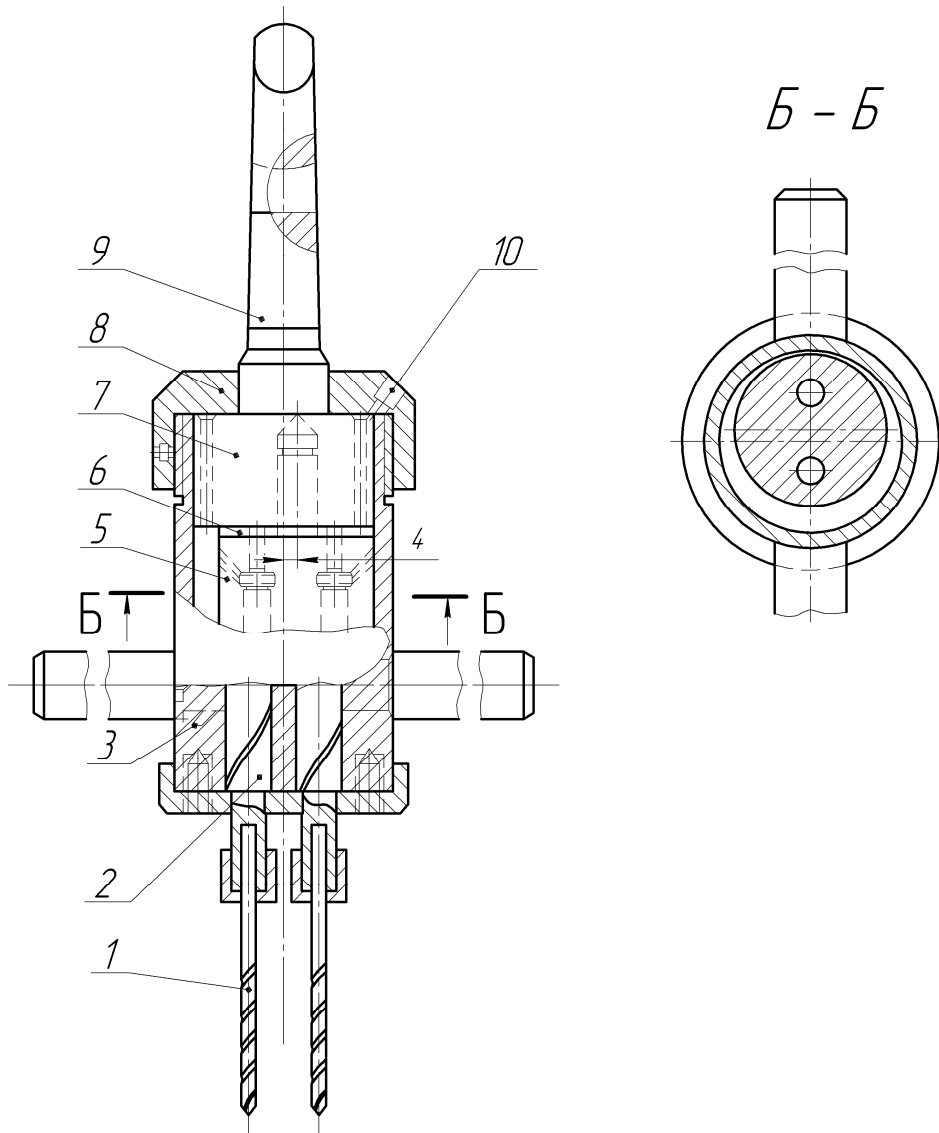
Будова багатошпindelної головки без зубчастих коліс: 1 – свердла; 2 – шпindel; 3 – корпус; 4 – стрижень; 5 – деталь; 6 – шайба бронзова; 7 – фланець; 8 – кришка; 9 – хвостовик; 10 – пробка
